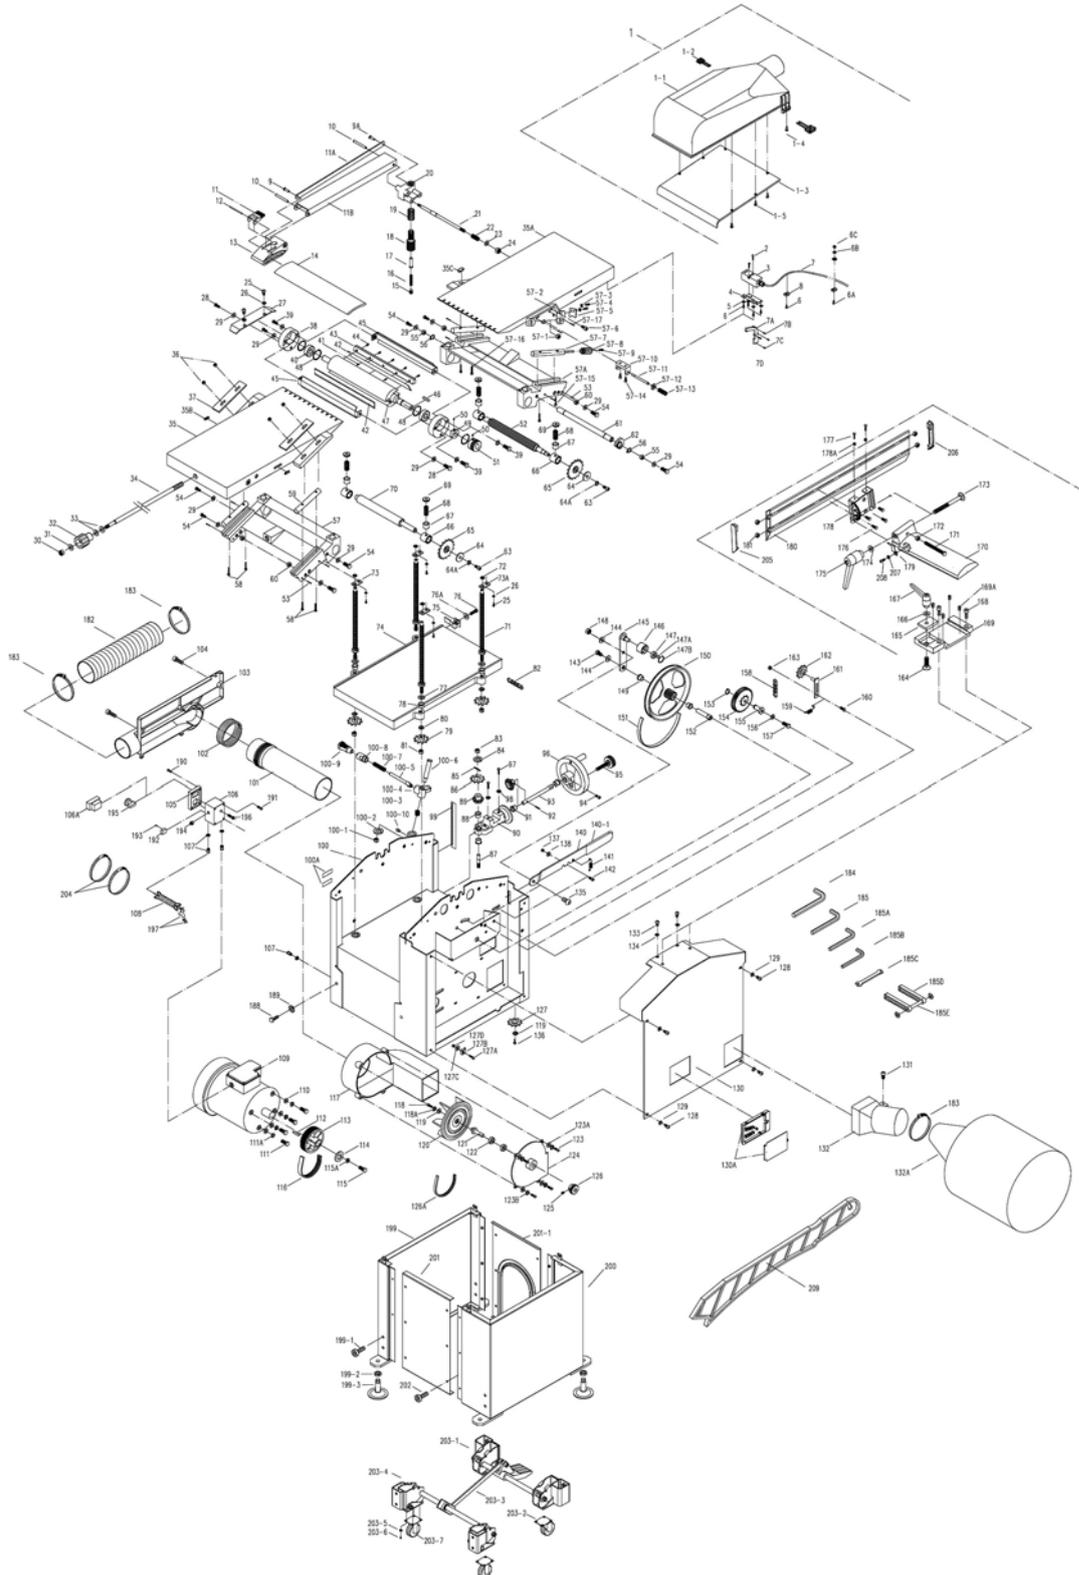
Plano de repuestos Cepilladora-Regresadora ADH 2540
